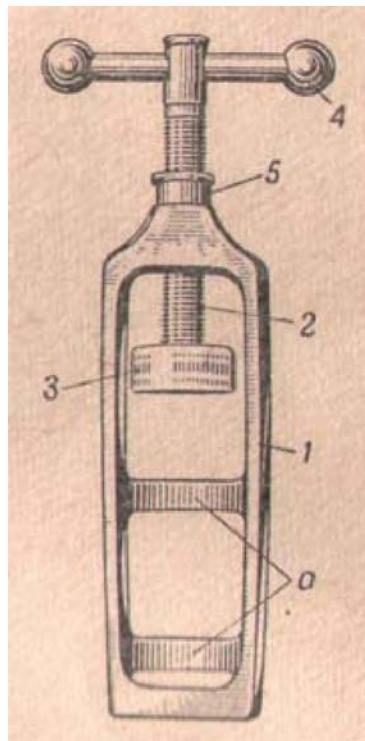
Закрутка ручная: 1-корпус закрутки; а - ребра-ограничители; 2 - винт-шпиндель; 3 - матрица; 4 - рукоятка; 5 - гайка винта-шпинделя. Настольная (рис. 50) и ручная (рис. 51) закрутки служат для закрепления дробового пыжика путем закатки свободного края дульца бумажной гильзы. Настольные закрутки более удобны и производительны. Они прочнее и ровнее закручивают края дульца гильзы.
